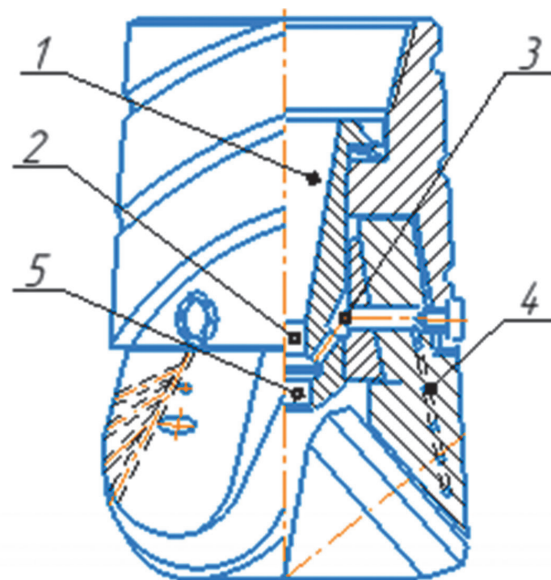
Разборное шарошечное долото: 1 – конфузор; 2 – насадка струйного насоса; 3 – канал инжекции; 4 – отверстие; 5 – гидромониторная насадка [8]
